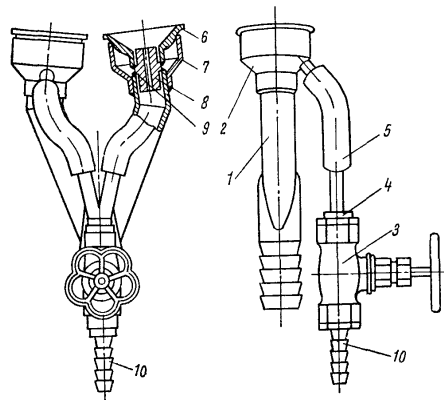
Сопло с приспособлением для гидropескоструйной очистки:
